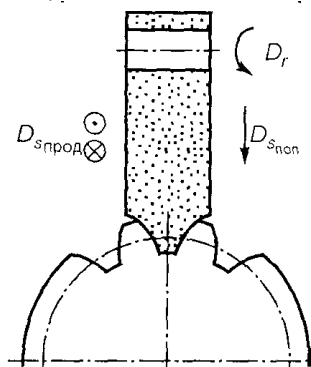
Схема шлифования впадины зубьев дисковым профильным кругом
